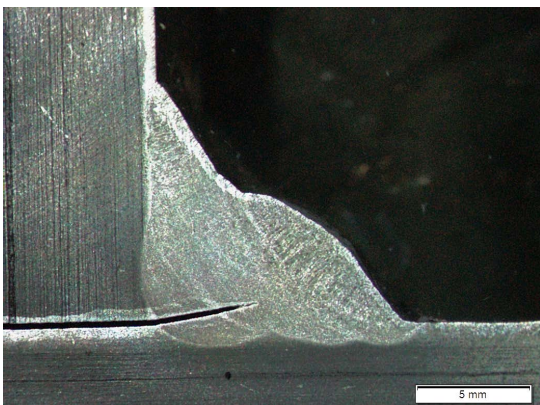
Probe G03-05, Schweißnaht FAT 71, einseitig geschweißt, Durchläufer
